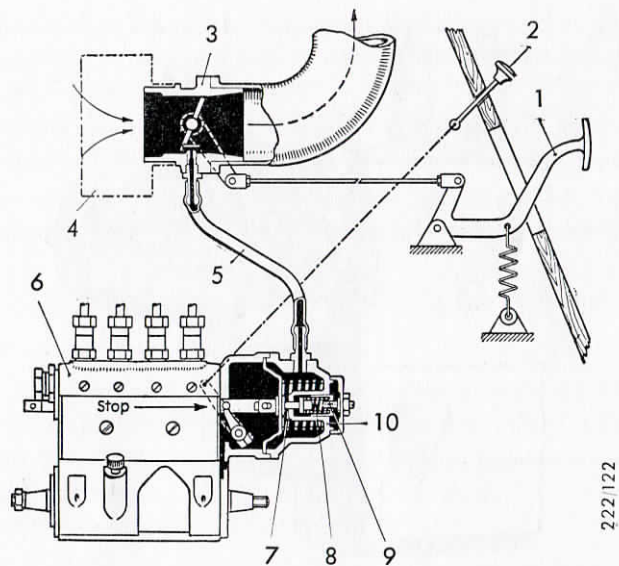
Schematisk bild av vakuumpregulator (läge för tomgång)
